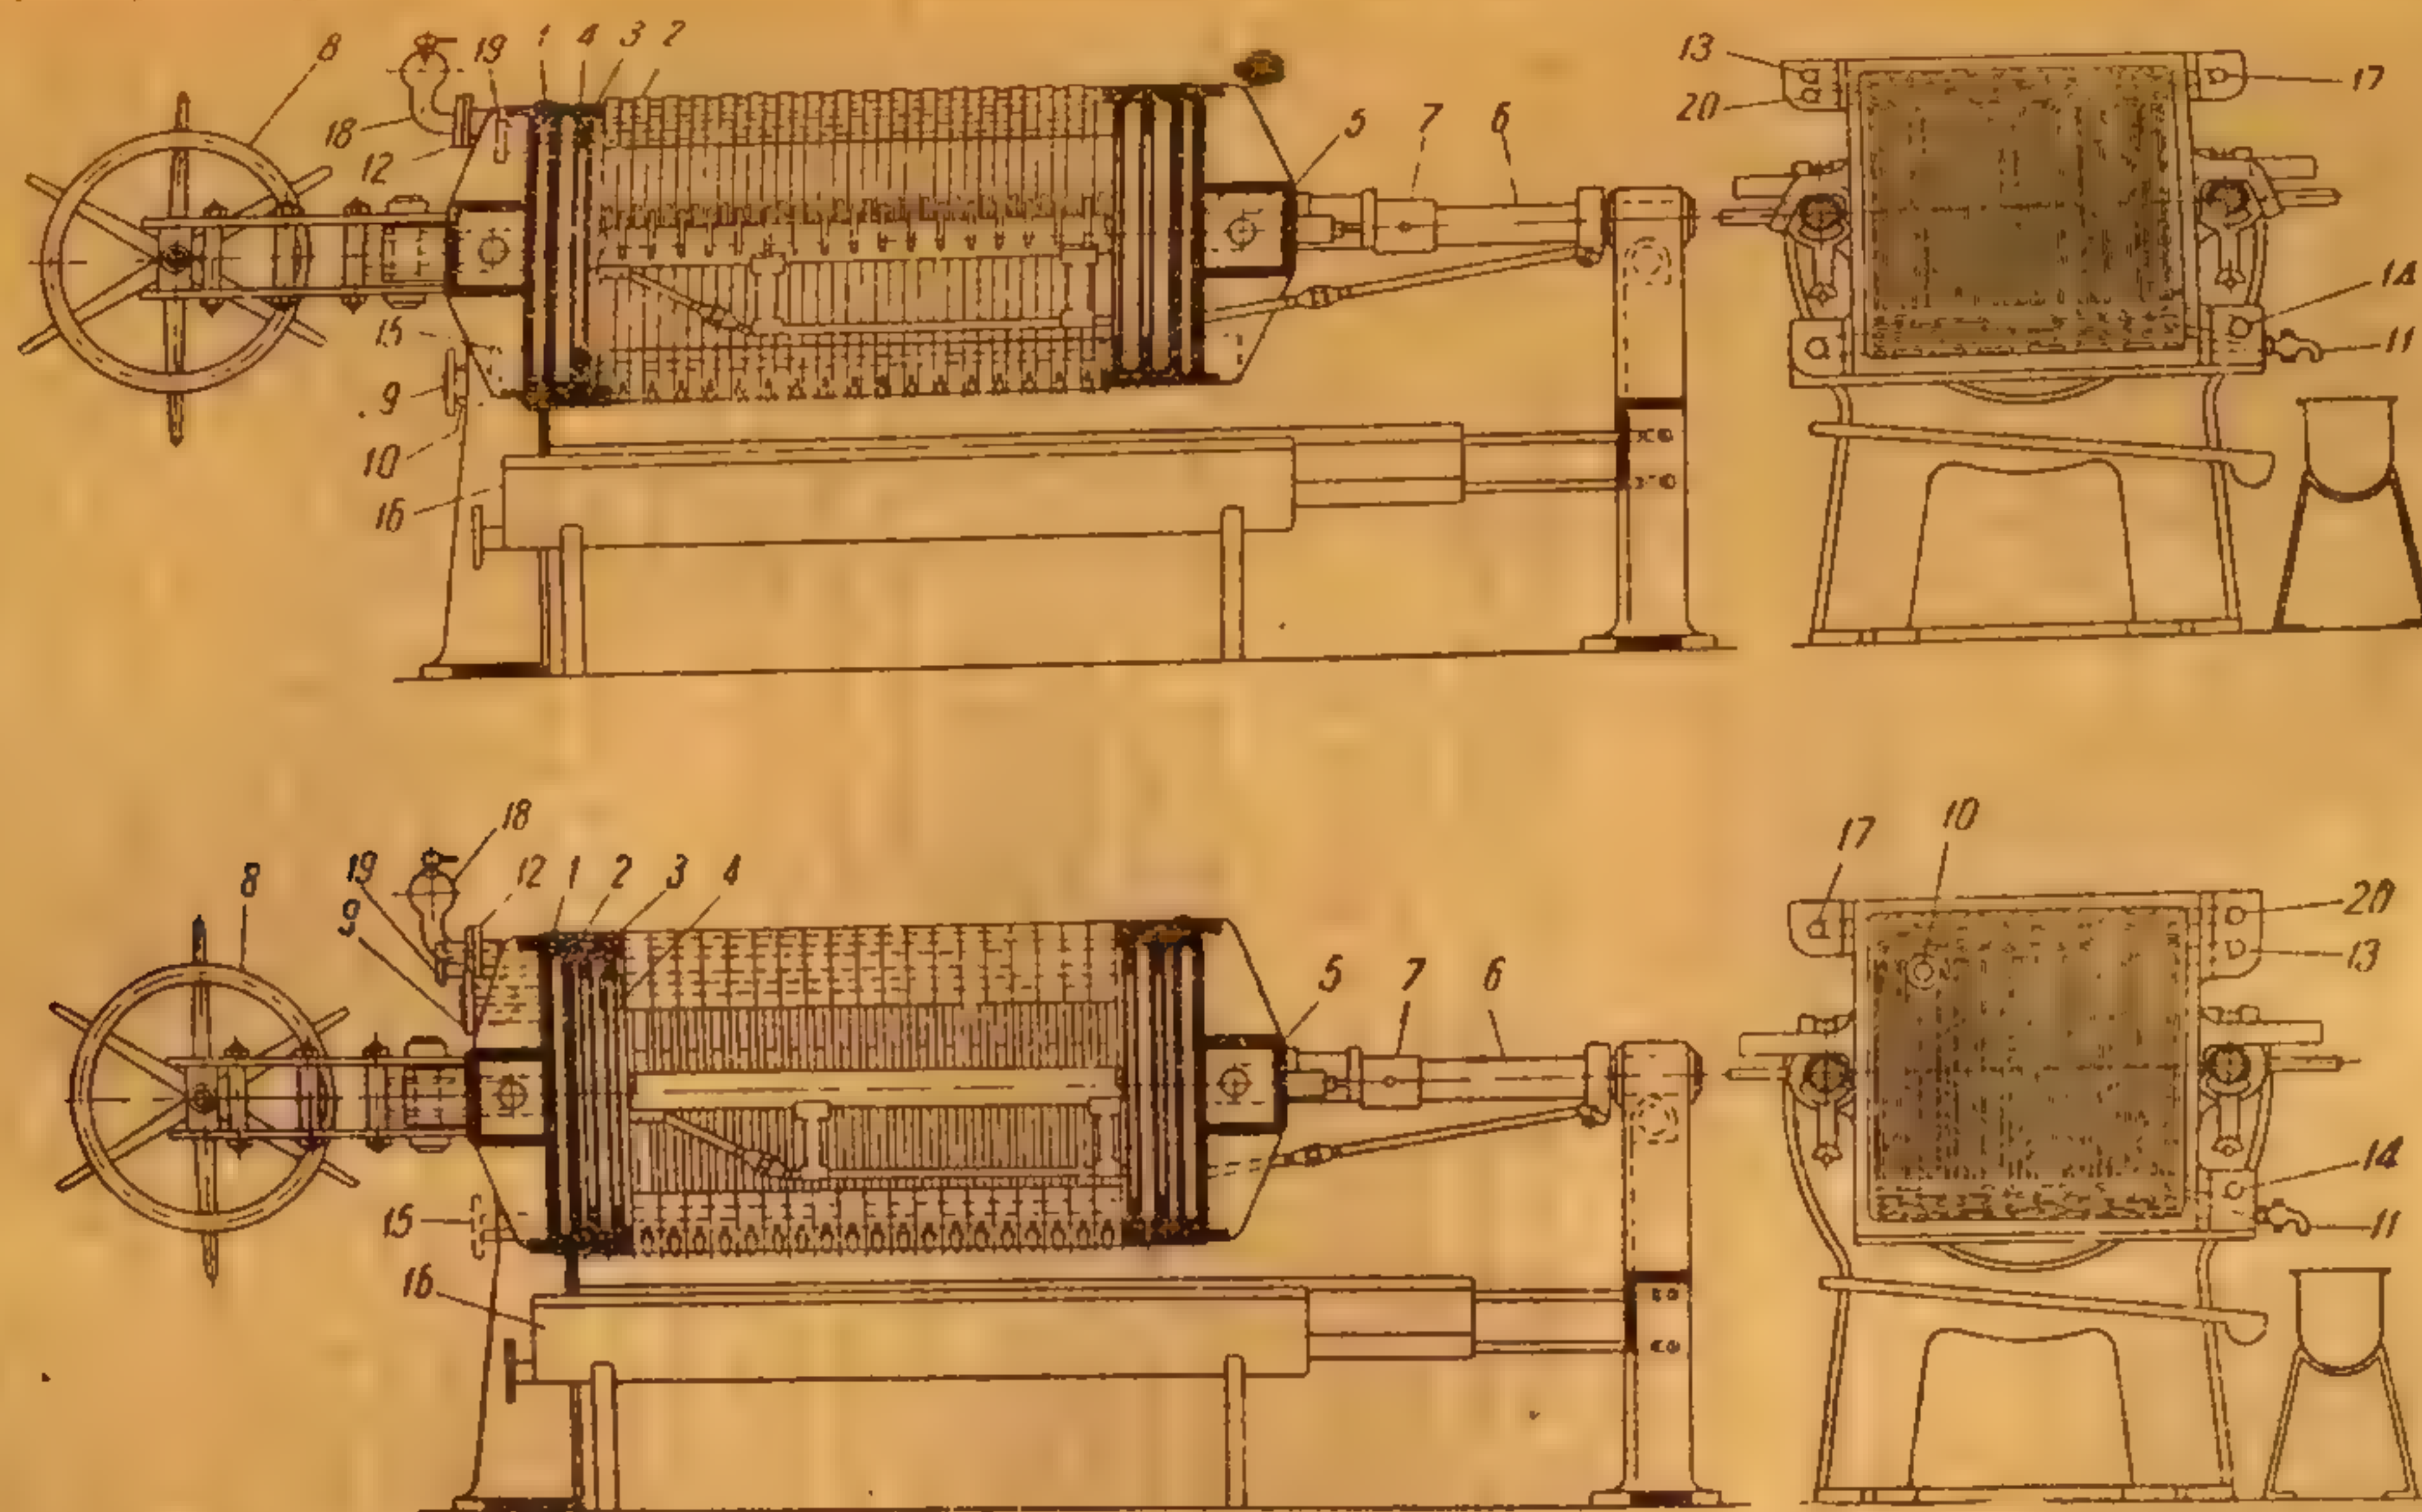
Камерный и рамочный фильтрпрессы. Вверху:
